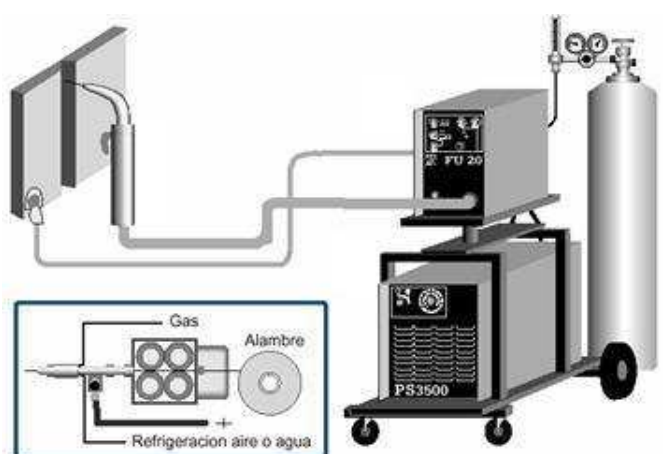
Diagrama esquemático del equipo de soldadura GMAW
